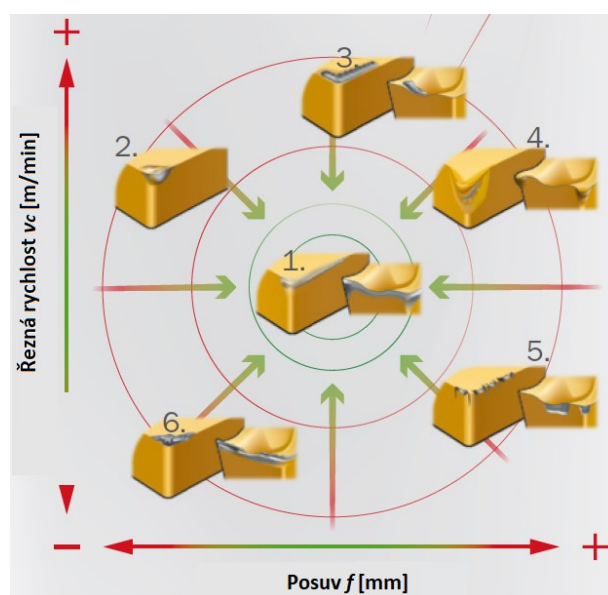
Mechanismy opotřebení řezných nástrojů¹⁴
